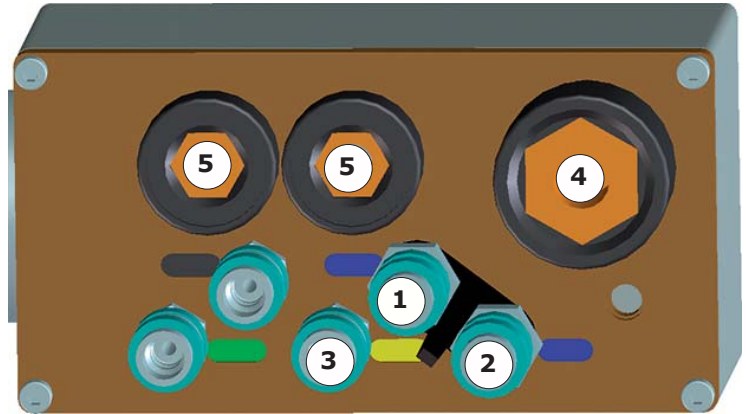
Block mit Anschlüssen für das Schlauchpaket des WIG-Brenners WP27
